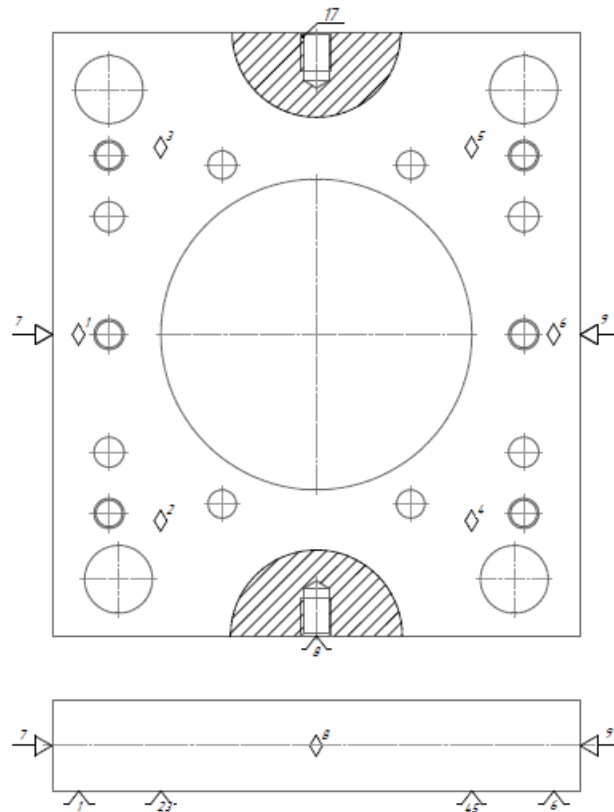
Схема базування та ескізи обробки на операцію 050
